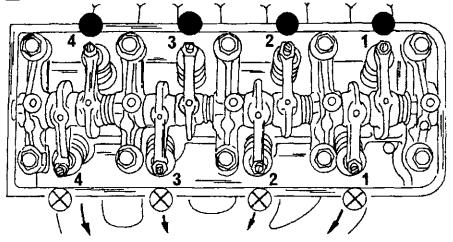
Собранный механизм коромысел. Черными кружками помечены впускные клапана, а кружками с крестами — выпускные клапана.
